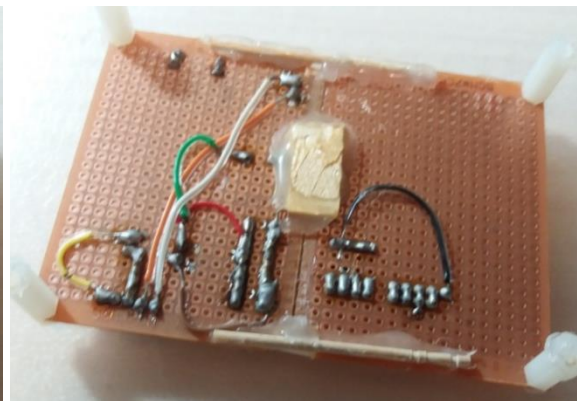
Vista del darrere de la placa de distribució d'energia. Tots els pins anomenats en la imatge anterior han estat soldats en aquesta cara de la placa juntament amb cables per tal de distribuir l'energia de la forma que es vulgui. Aquestes soldadures s'han fet amb un soldador d'estany⁷⁹.
